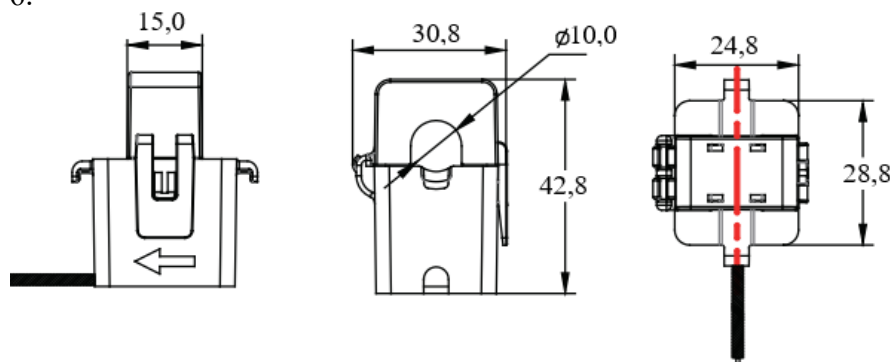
Внешний вид и габаритные размеры датчика SCT05
